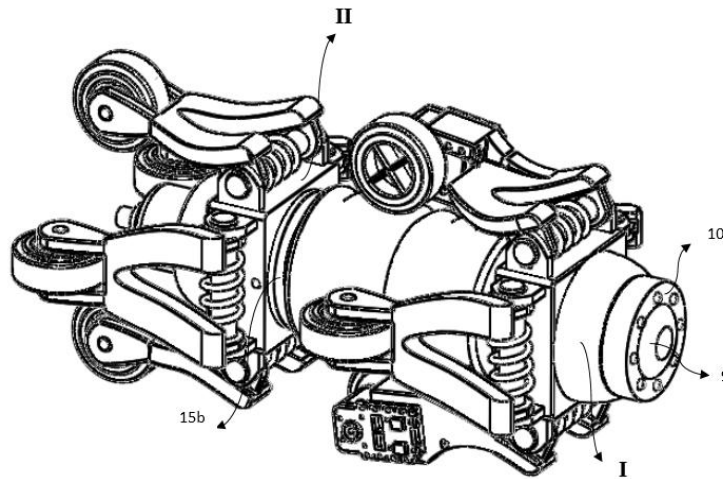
Diseño CAD del robot. Posición extremidades retraídas. (Vista isométrica)
